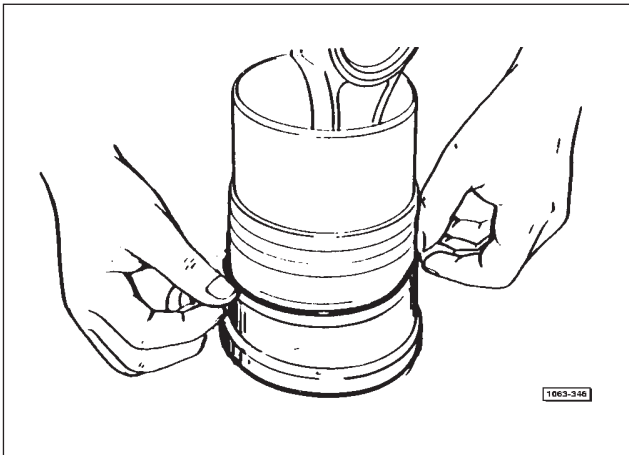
Mise en place des joints toriques sur le cylindre.
